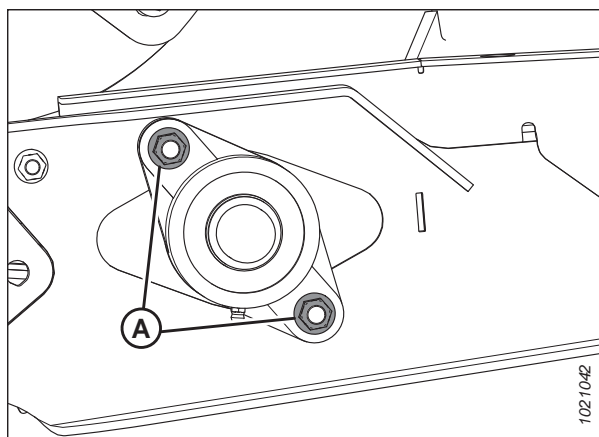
Подшипник приводного ролика подающего полотна
